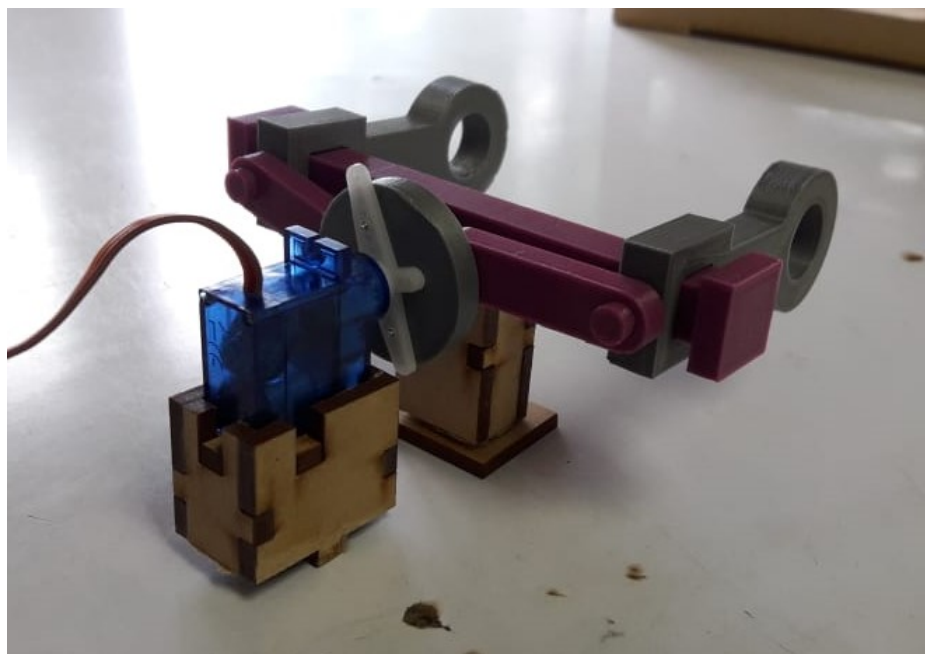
Vista posterior del mecanismo de posicionamiento manufacturado
